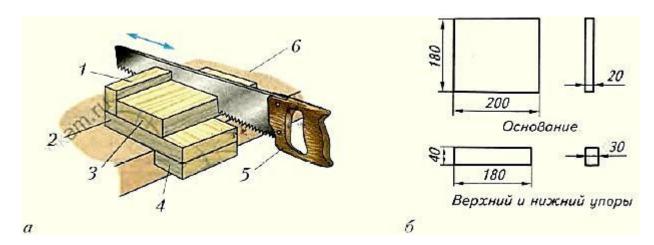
Пиление с помощью приспособления (a): 1 — верхний упор; 2 — основание; 3 — заготовка; 4 — нижний упор; 5 — ножовка; 6 — верстак; эскизы деталей приспособления (б)
